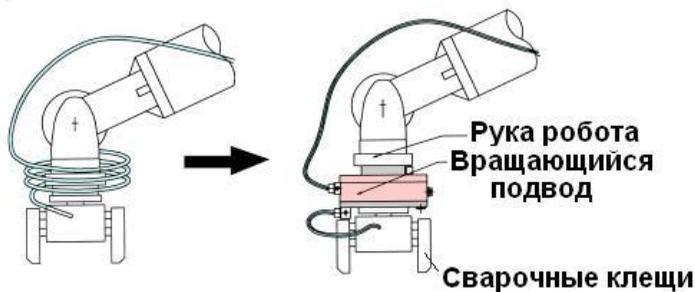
Схемы передачи энергии к сварочным клещам.
